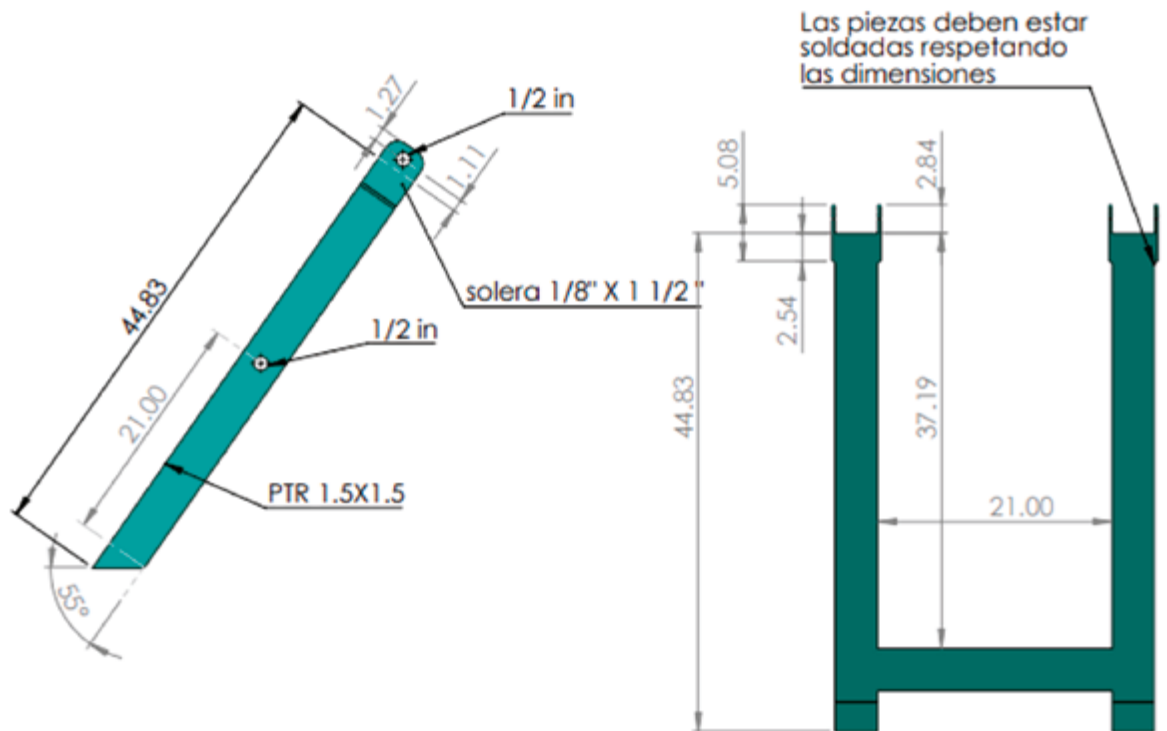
Especificaciones para la construcción del elemento A (dimensiones en cm).
